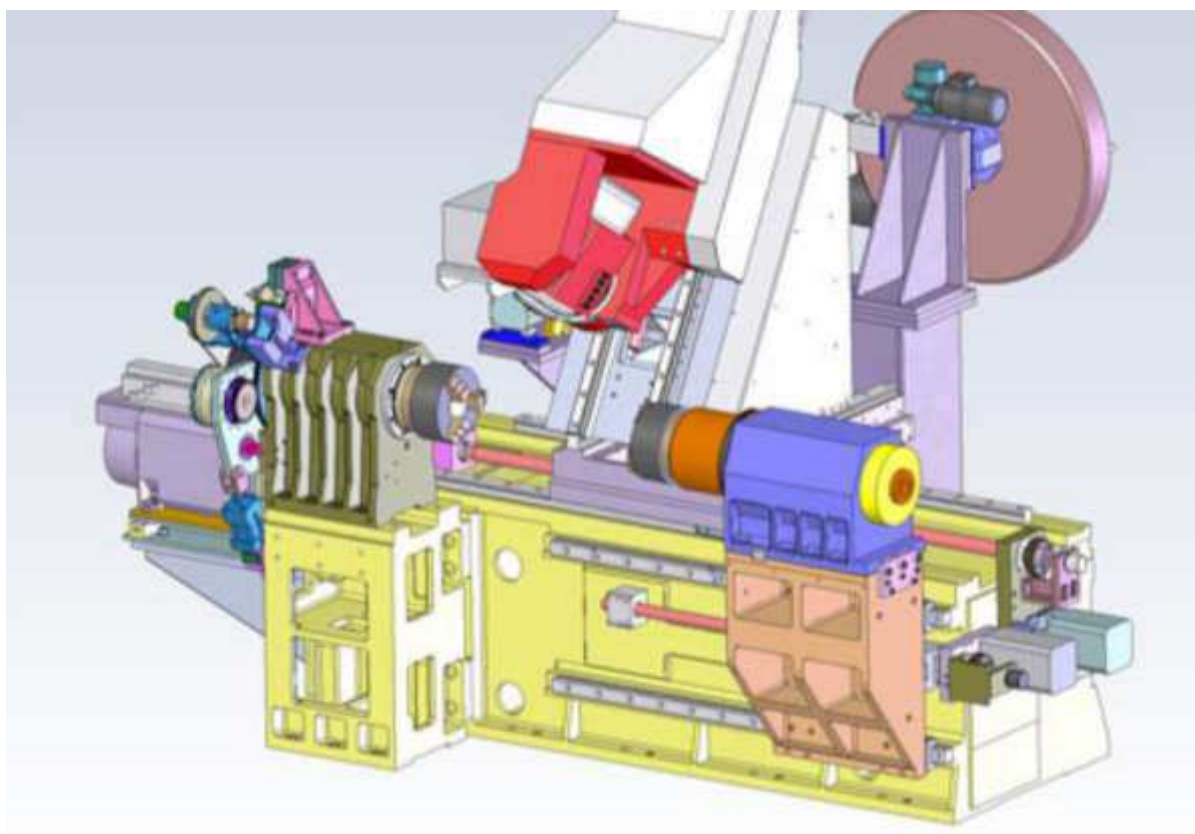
Основные узлы токарно-фрезерного обрабатывающего центра 1728С
